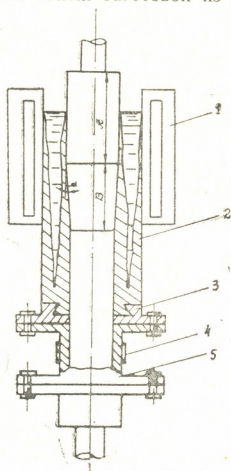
Схема устройства для определения вытягивания заготовки из кристаллизатора: 1 — кристаллизатор; 2 — заготовка; 3 — «ласточкин хвост»; 4 — тензодатчик; 4 — затравка
